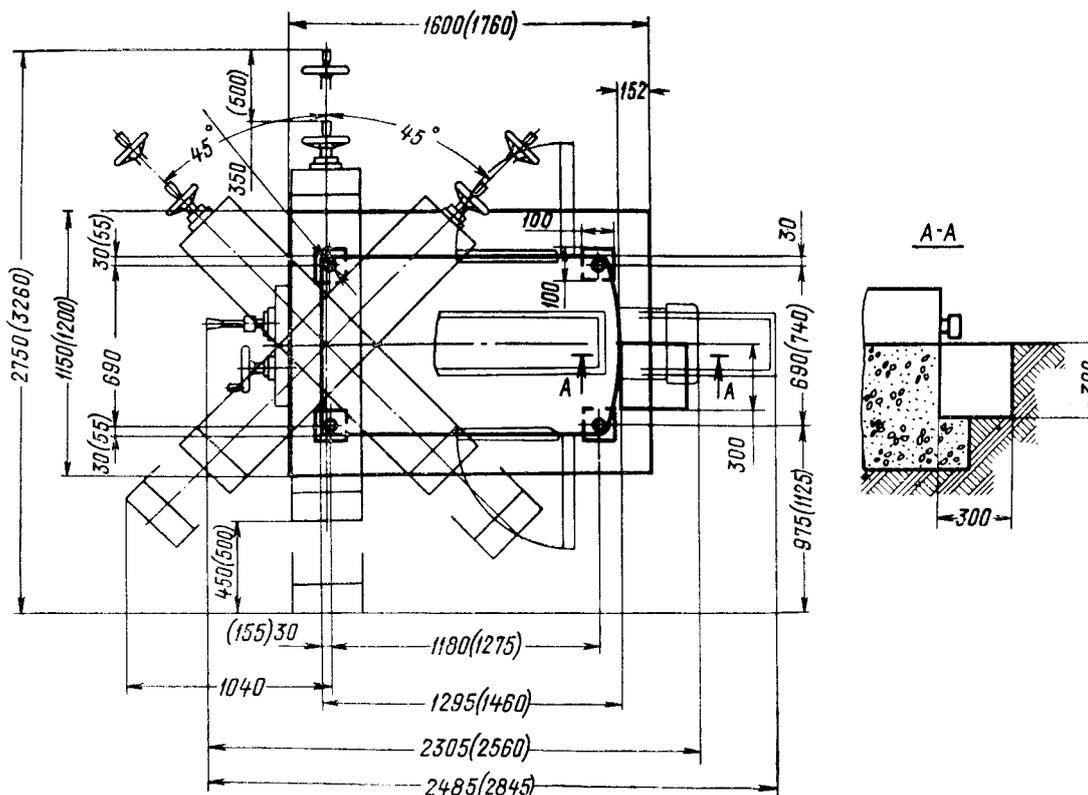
Установочный чертеж станков 6P82, 6P83 (размеры в скобках приведены для станка 6P83)
